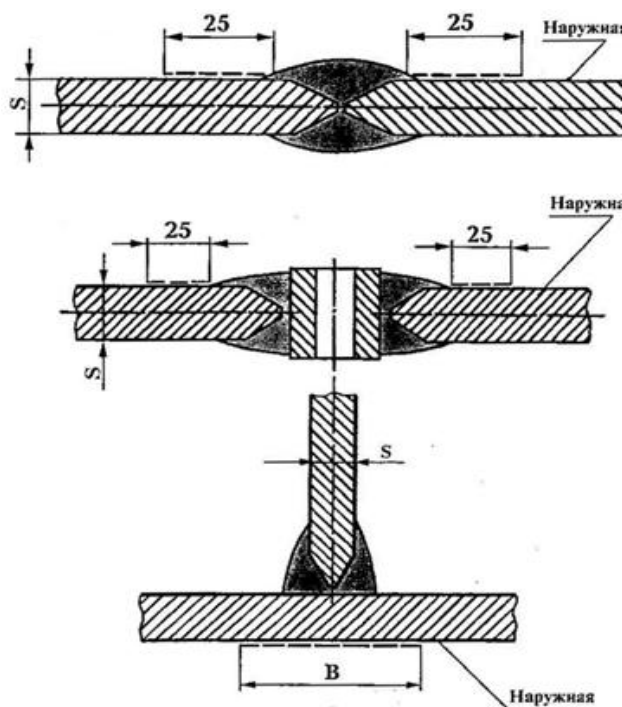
Схема обработки сварного соединения УУО с наружной стороны
